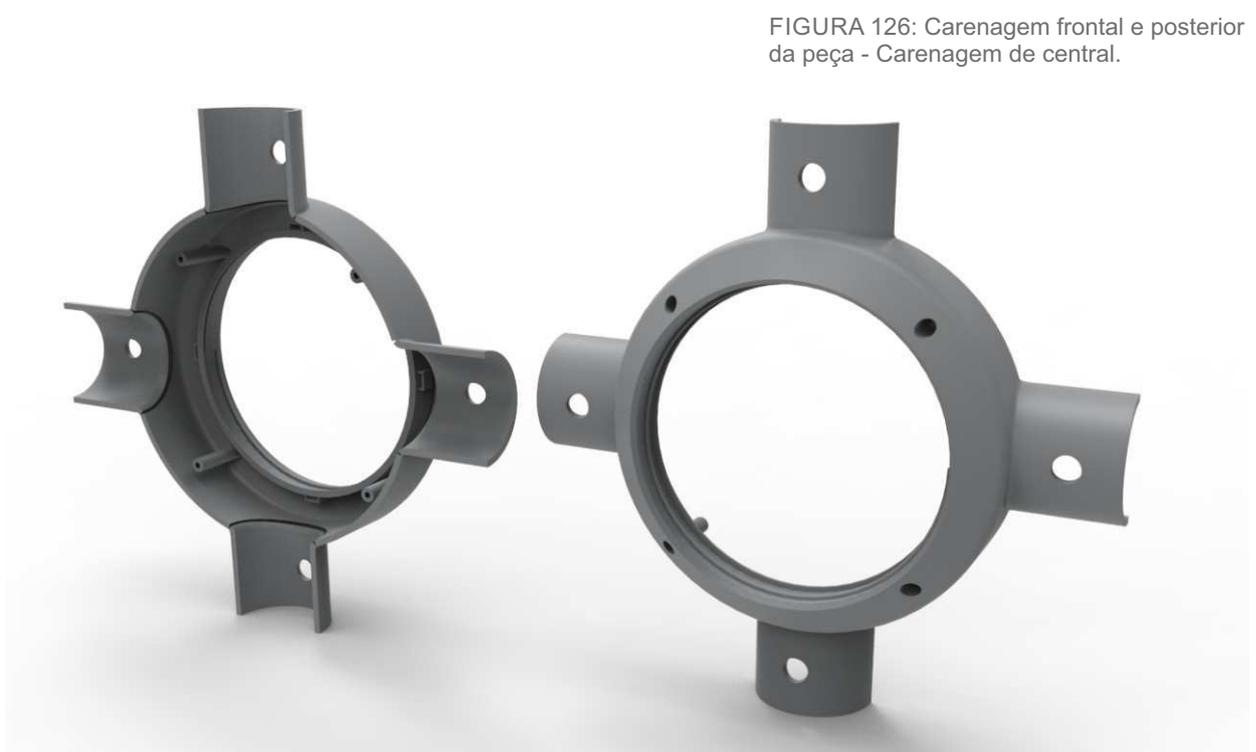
Carenagem frontal e posterior da peça - Carenagem de central.
